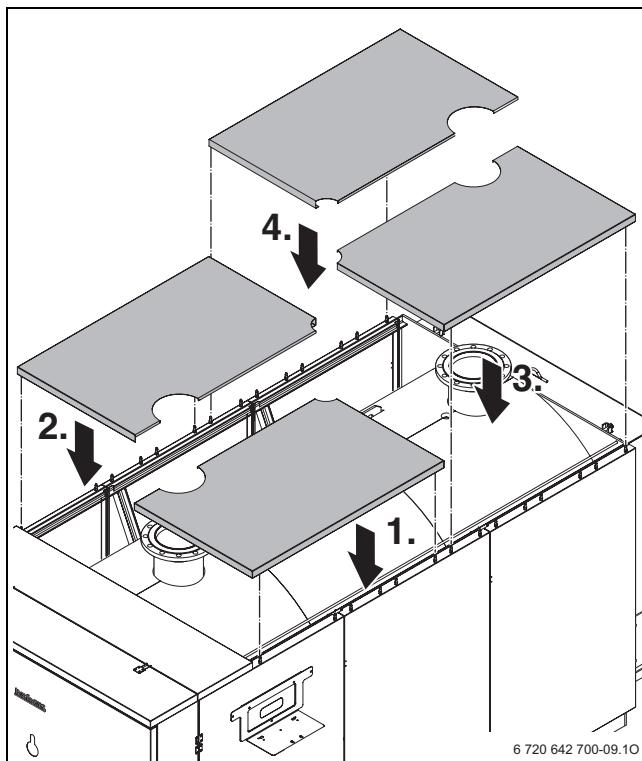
Монтаж боковых верхних крышек на котлах 1400 - 1850 кВт
